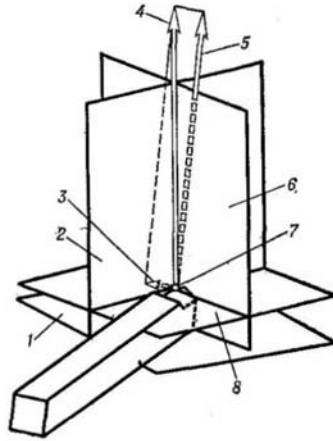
Эффективная система баз отсчета углов режущего клина (у токарного резца):
